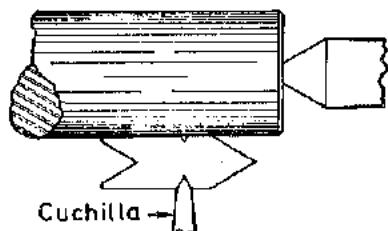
Para situar la herramienta perpendicular al eje de la pieza, se utiliza una galga de puntos de centrado y perfiles de rosca (South Bend Lathe Works).
